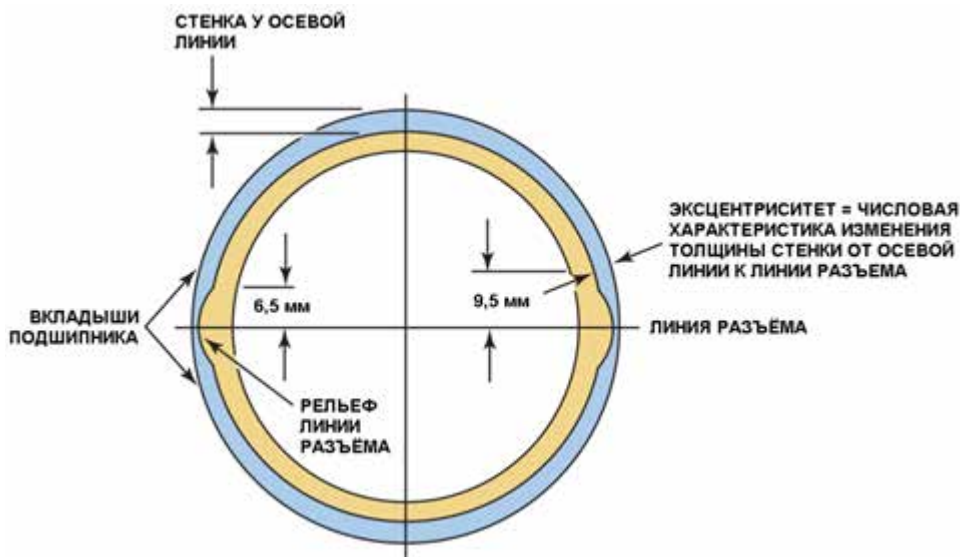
Толщина несущей стенки не одинакова от центра к линии разреза. Это называется эксцентricностью, и используется, чтобы помочь создать масляный клин между шейкой и подшипником; источник: *Pearson Education, Inc.
